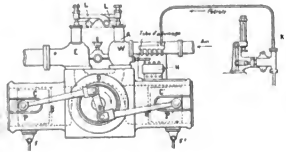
Motor und Explosionskammern des Wagens Koch.
